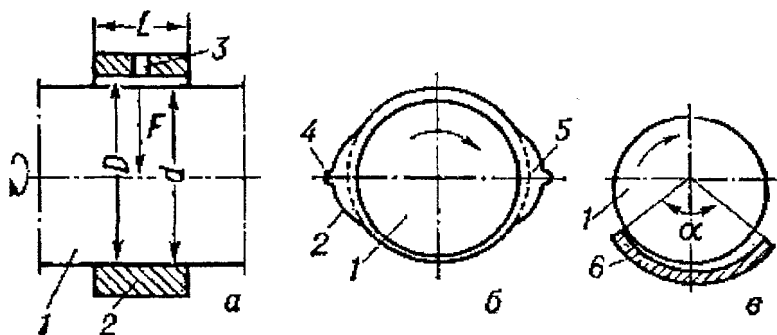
Схемы узла с радиальным подшипником скольжения: *а* – с подводом смазки через отверстие во вкладыше; *б* – разрез подшипникового узла с масляными карманами; *в* – с вкладышем частичного охвата; 1 – вал; 2 – втулка (вкладыш); 3, 4 – отверстия для подачи смазки; 5 – масляные карманы; *б* – вкладыш с углом охвата  $\alpha$ ; *F* – радиальная нагрузка; *L* – ширина вкладыша; *D* – внутренний диаметр вкладыша; *d* – диаметр шейки вала
